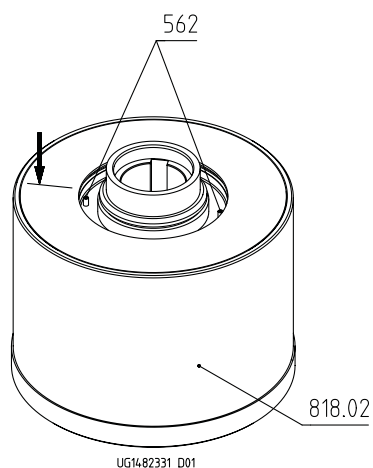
Маркировка положения штифта 562 на фланце внешнего ротора 818.02
